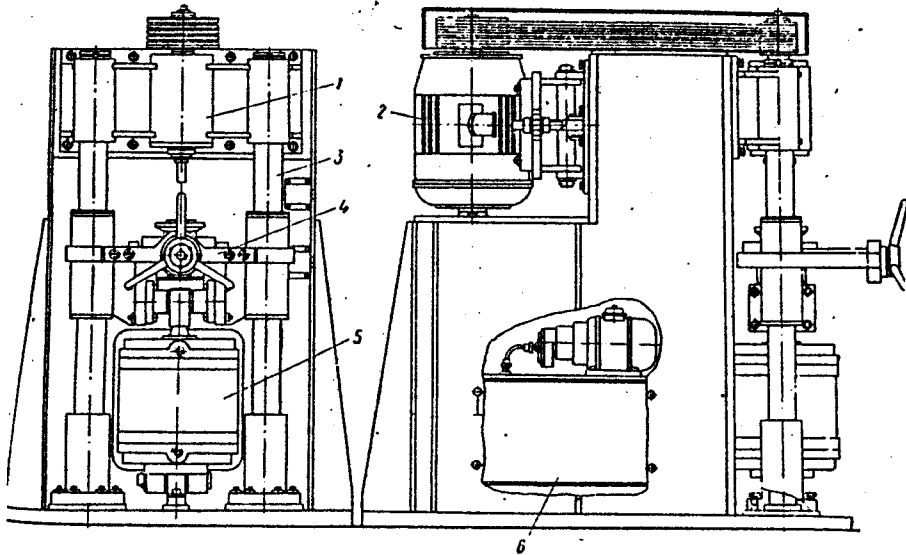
Общий вид установки для наплавки металлов и сплавов трением
